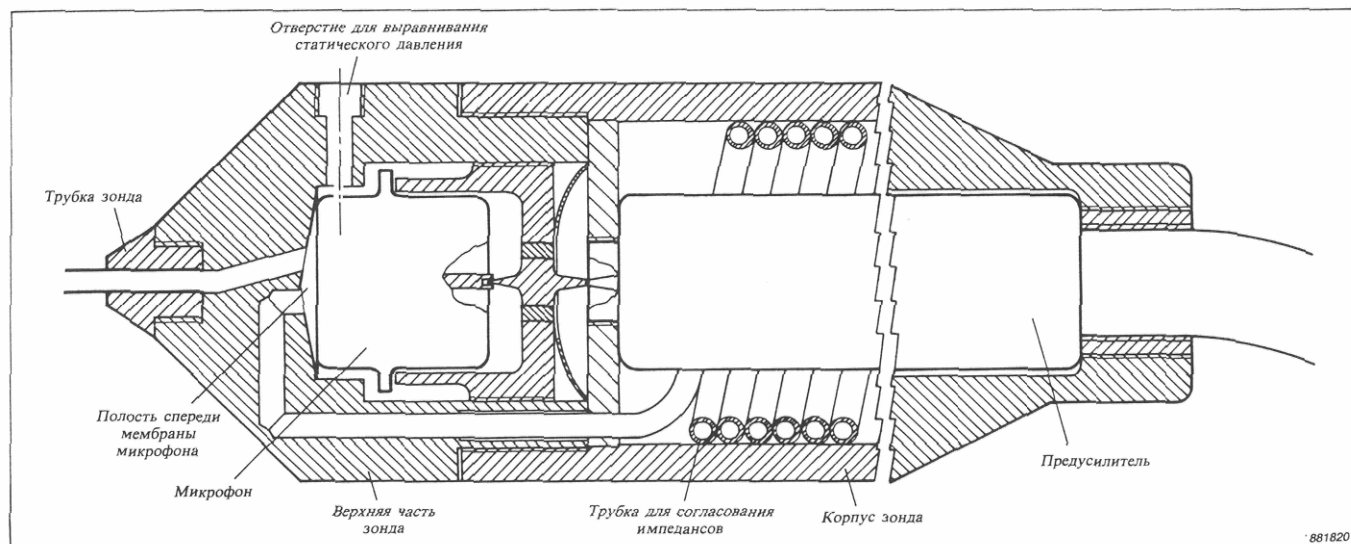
Схематический чертеж (вид в разрезе), иллюстрирующий конструкцию микрофонного зонда 4182
